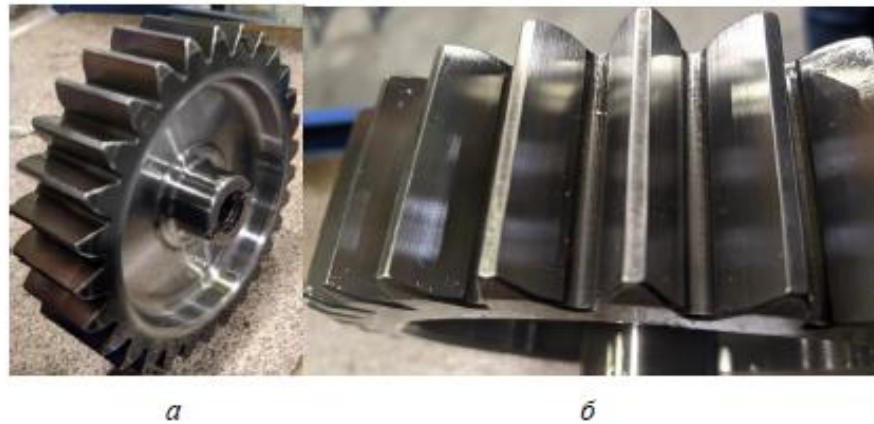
Циліндричне зубчасте колесо: а – загальний вигляд; б – вид зверху
